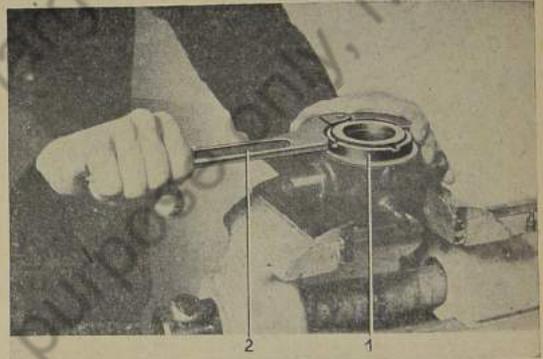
Verschraubung aus Lagergehäuse herausschrauben
